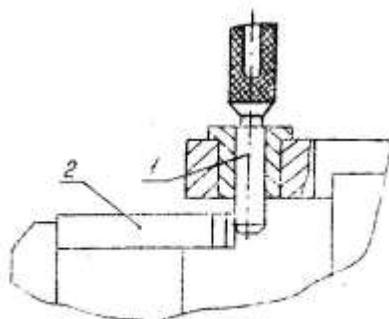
Схема настройки УСП-кондуктора: 1 — контрольный валик; 2 — блок концевых мер
